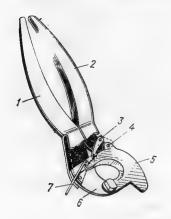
1 — ручка подвижная; 2 — трос; 3 — рычаг; 4 — корпус; 5 — матрица; 6 — сектор зубчатый; 7 — рейка с пуансоном; 8 — барабан
